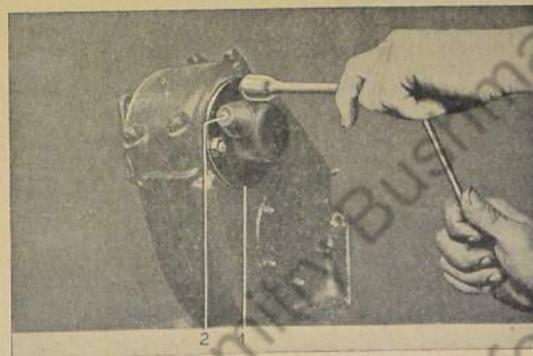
Verschlusskappe an Zwischenradgehäuse anschrauben
